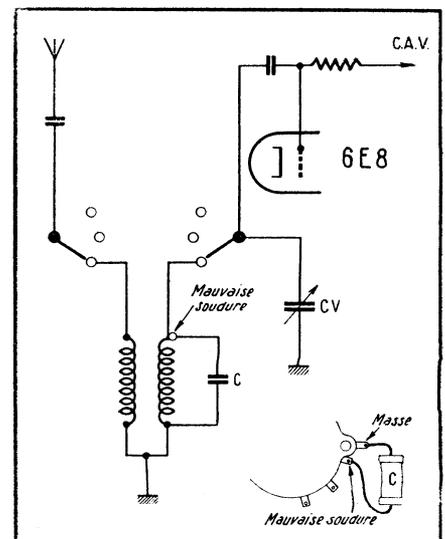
Crachements par mauvais contact du condensateur C, à cause d'une soudure défectueuse.
